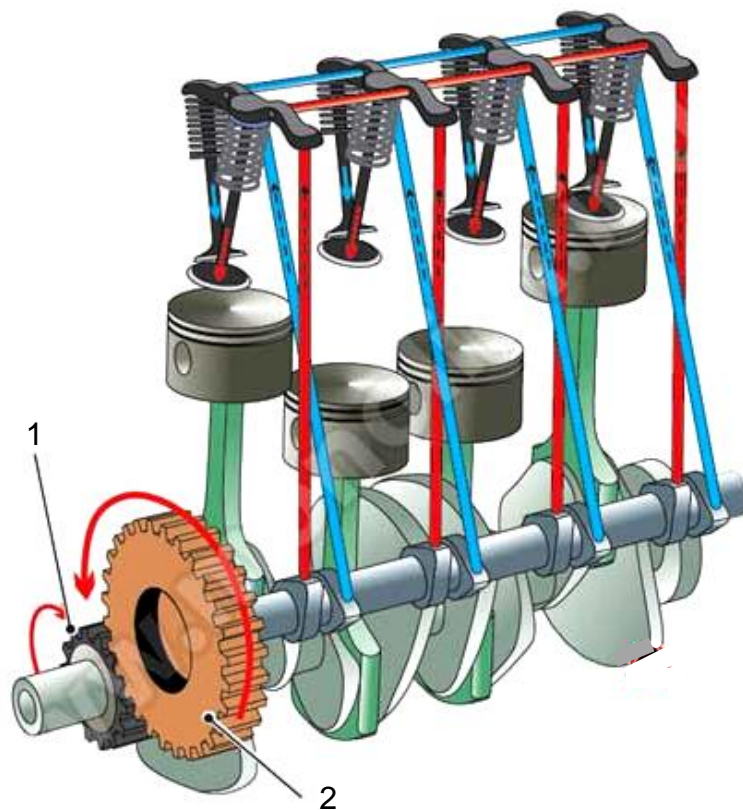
Схема шестеренного приводу газорозподільного механізму: 1 – шестерня колінчастого вала; 2 – шестерня розподільного вала
